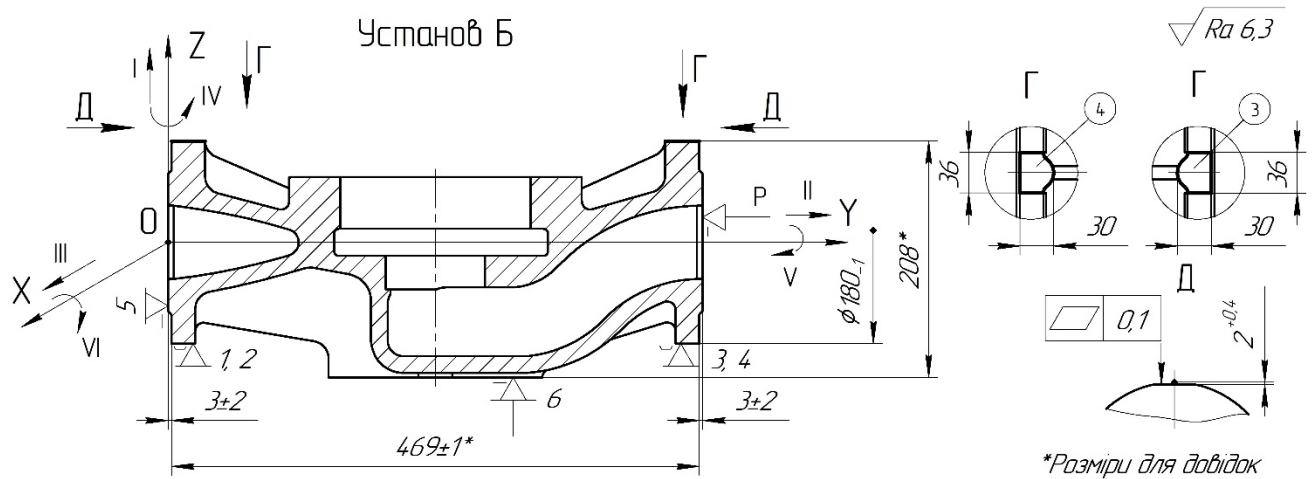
Схема установки заготовки на операції 020, Варіант 2, установ Б
